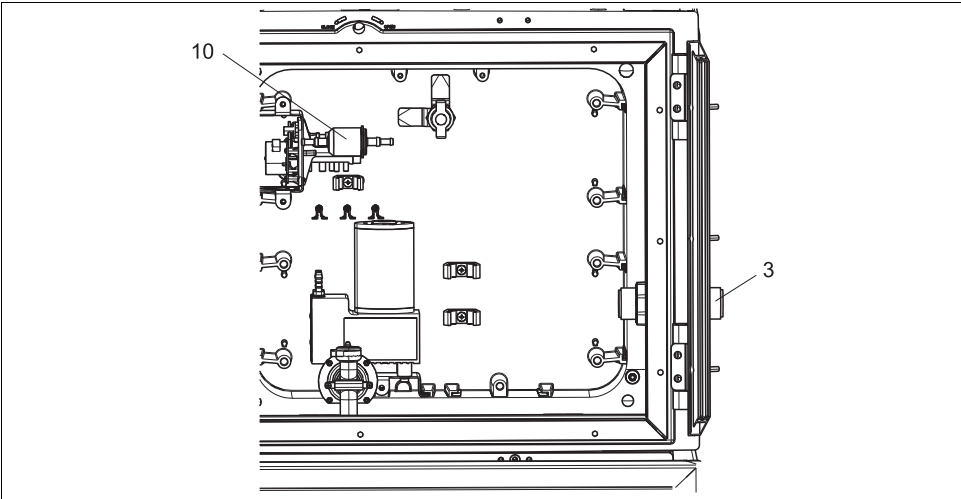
Ersatzteile für Ausführung mit Membranpumpe (Ansicht hinter der Pumpenhalterung)
